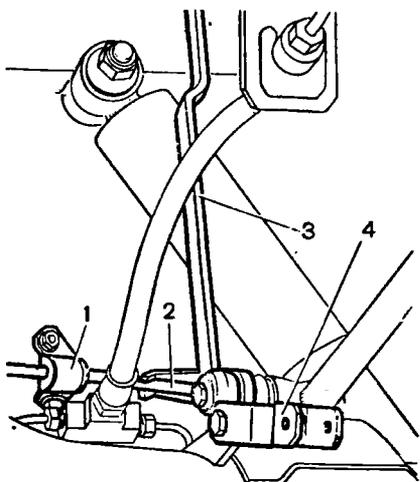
Установка приспособления 67.7820.9518 для регулировки регулятора давления задних тормозов: 1 - кронштейн привода регулятора давления; 2 - рычаг привода регулятора давления задних тормозов; 3 - приспособление 67.7820.9518; 4 - тяга соединения рычага привода регулятора давления с кронштейном балки заднего моста
